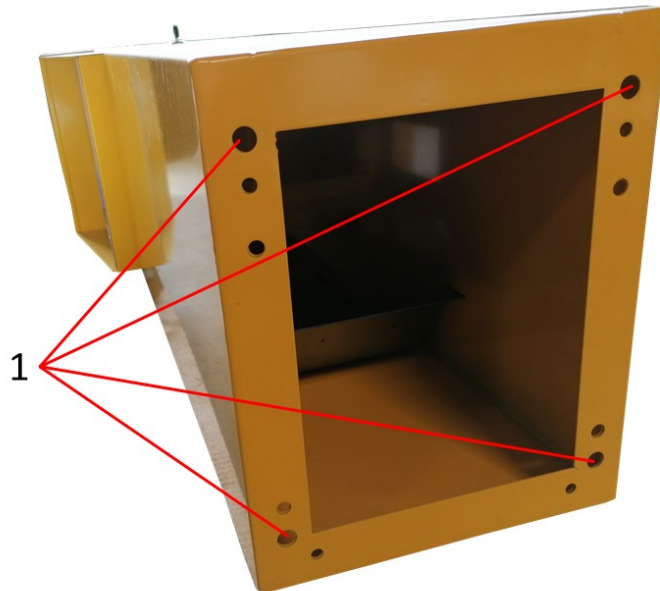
Fußplatte Terminalgehäuse mit Befestigungsbohrungen (1)
